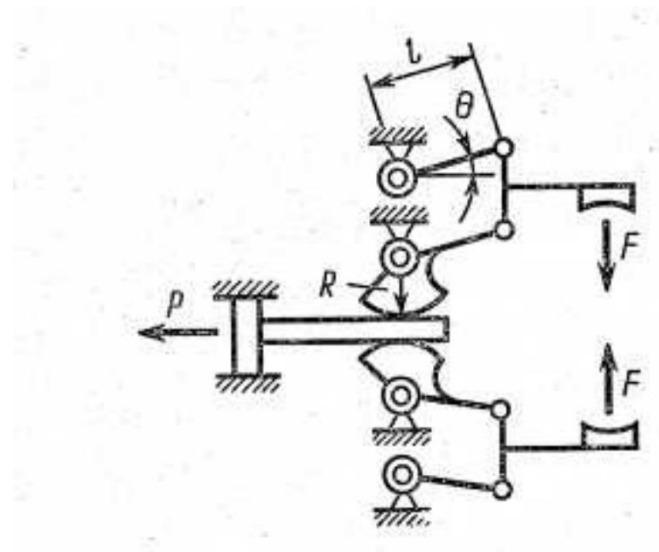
Розрахункова схема захоплювального пристрою
